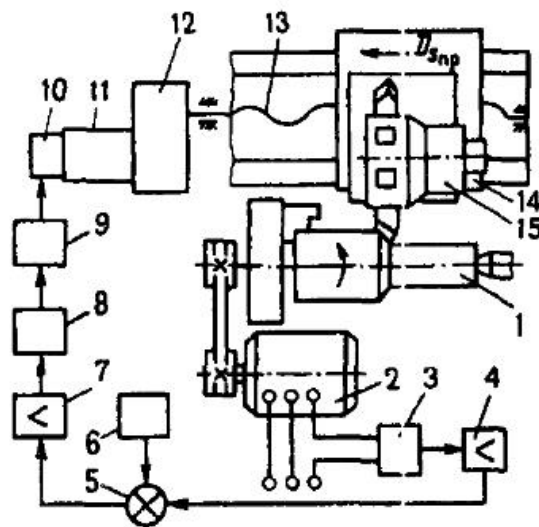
Схема обробки заготовки на токарному верстаті з адаптивною системою ЧПК
